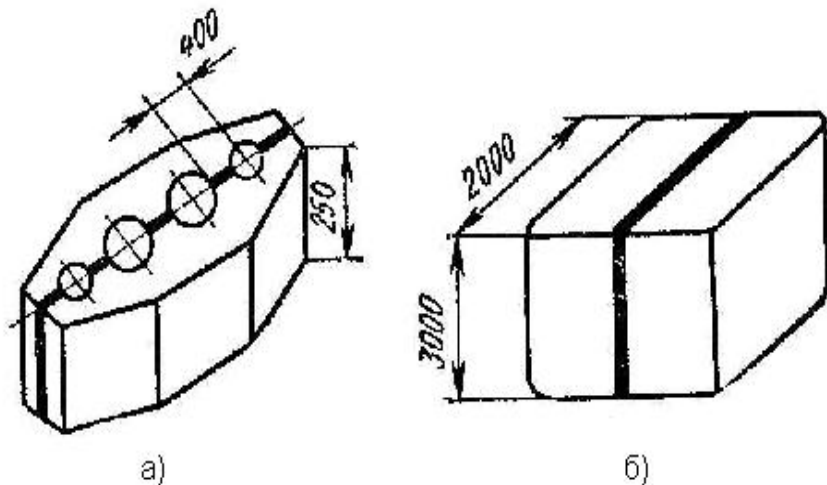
Примеры применения электрошлаковой сварки:
